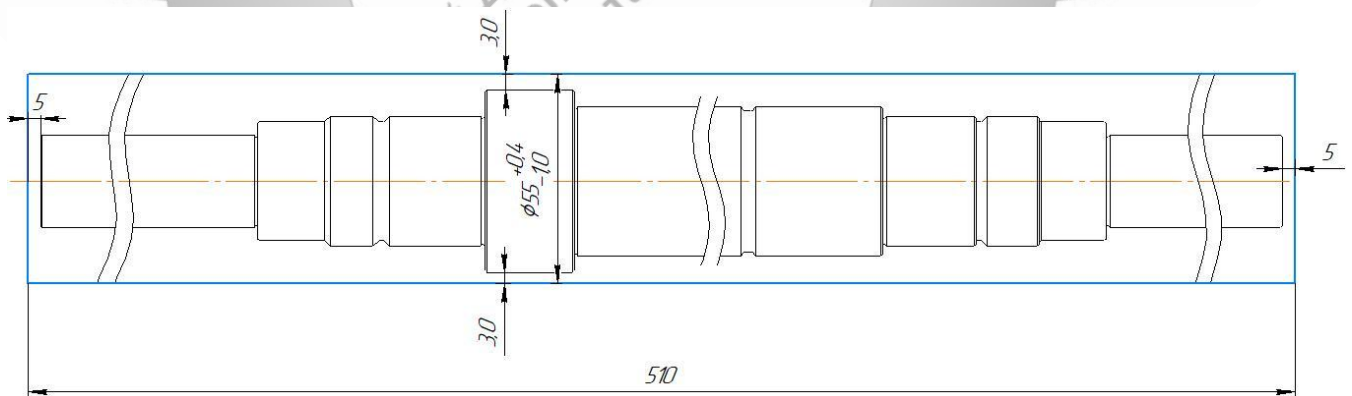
Заготовка, яка виготовлена із круглого прокату
